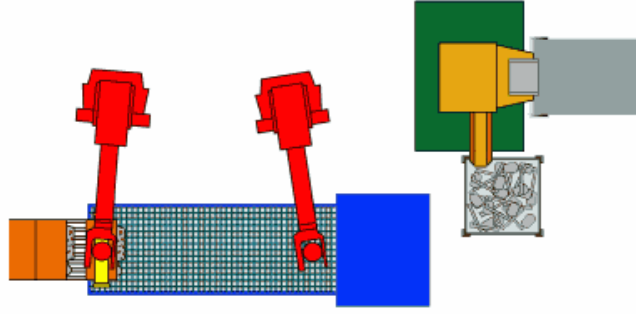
Disacool soğutma tamburu (Disa, 2004)
